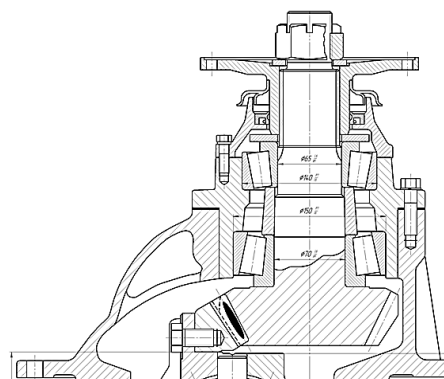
Конструктивная схема редуктора ведущего моста транспортного средства – узел ведущей шестерни
